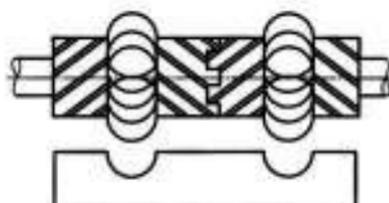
Фрезерование фасонной поверхности набором фрез
